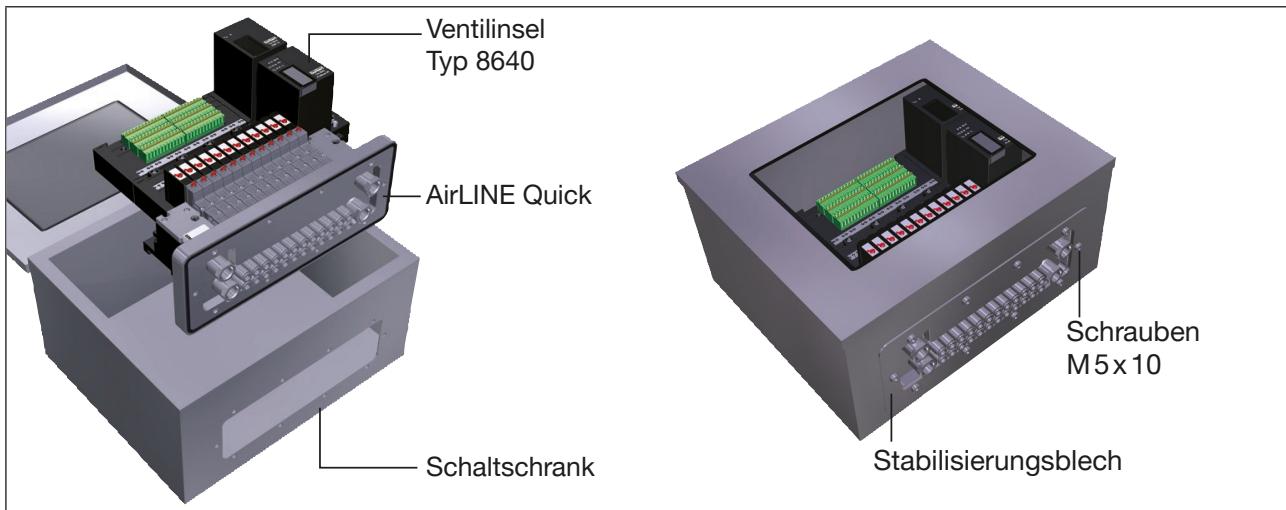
Platzieren der Ventilinsel im Schaltschrank und Befestigen des Stabilisierungsblechs
